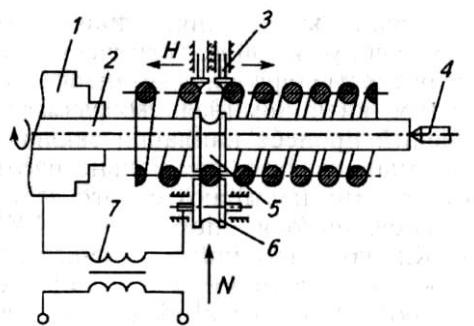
Схема установки для восстановления пружин накаткой:
